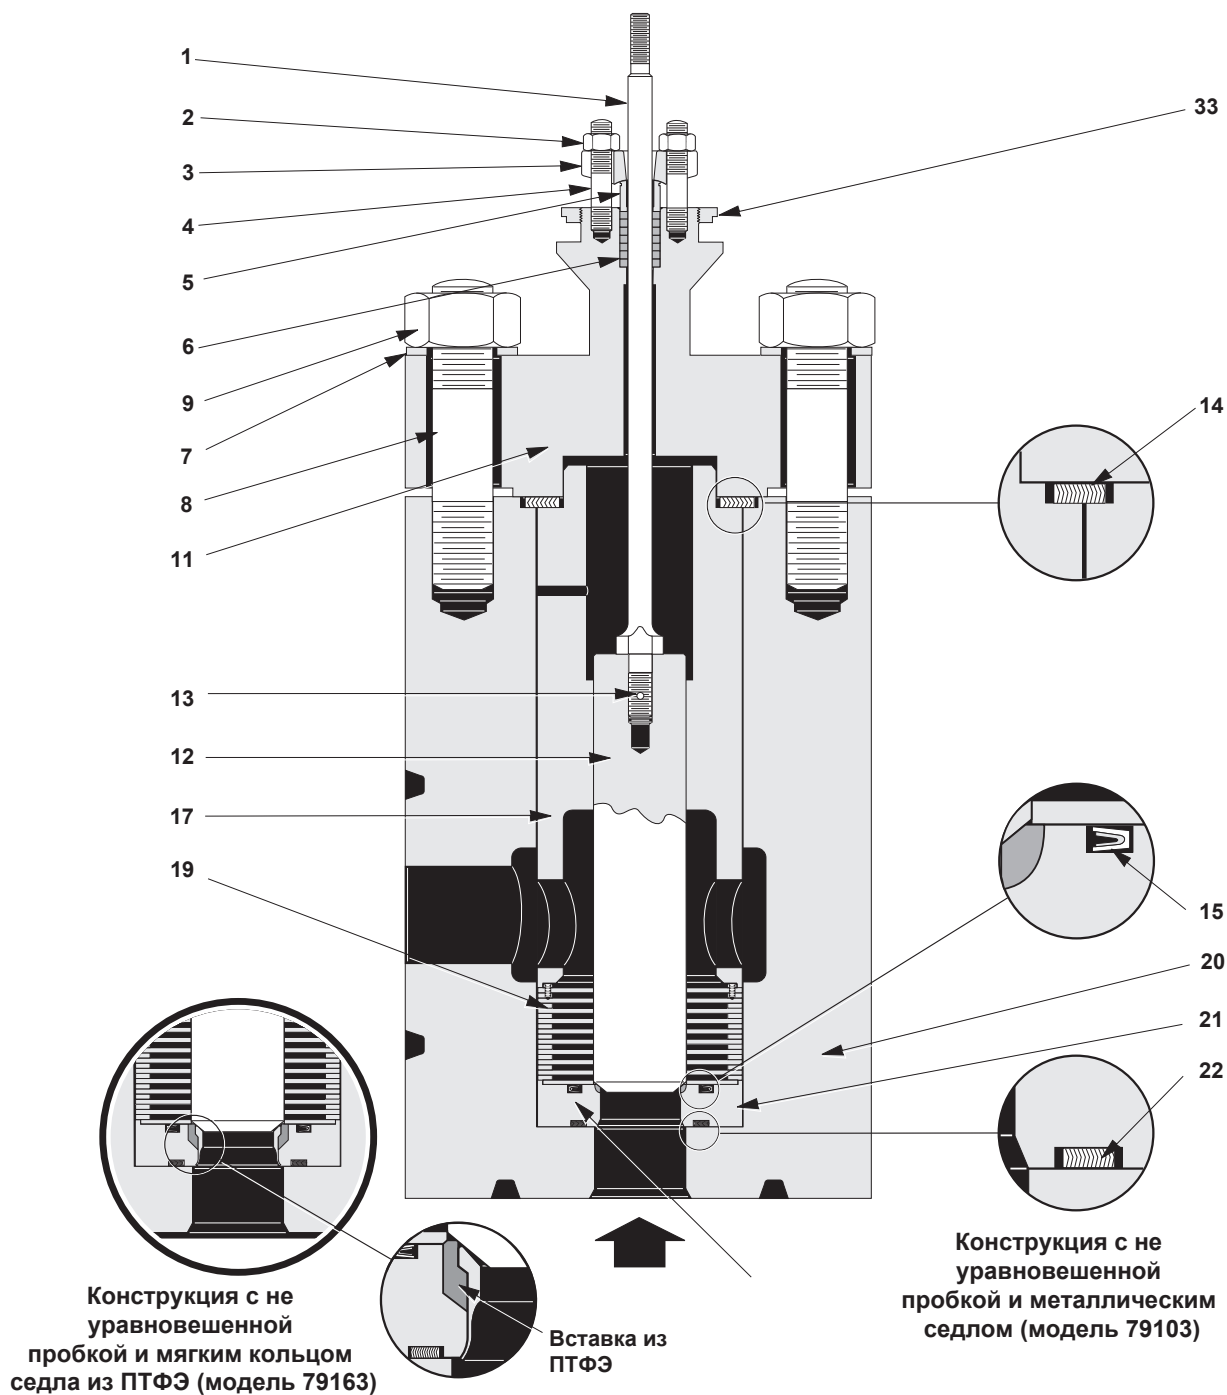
Поперечное сечение клапана VRT серии 79000 размером 1 и 1-1/2 дюйма с кованым блочным корпусом
